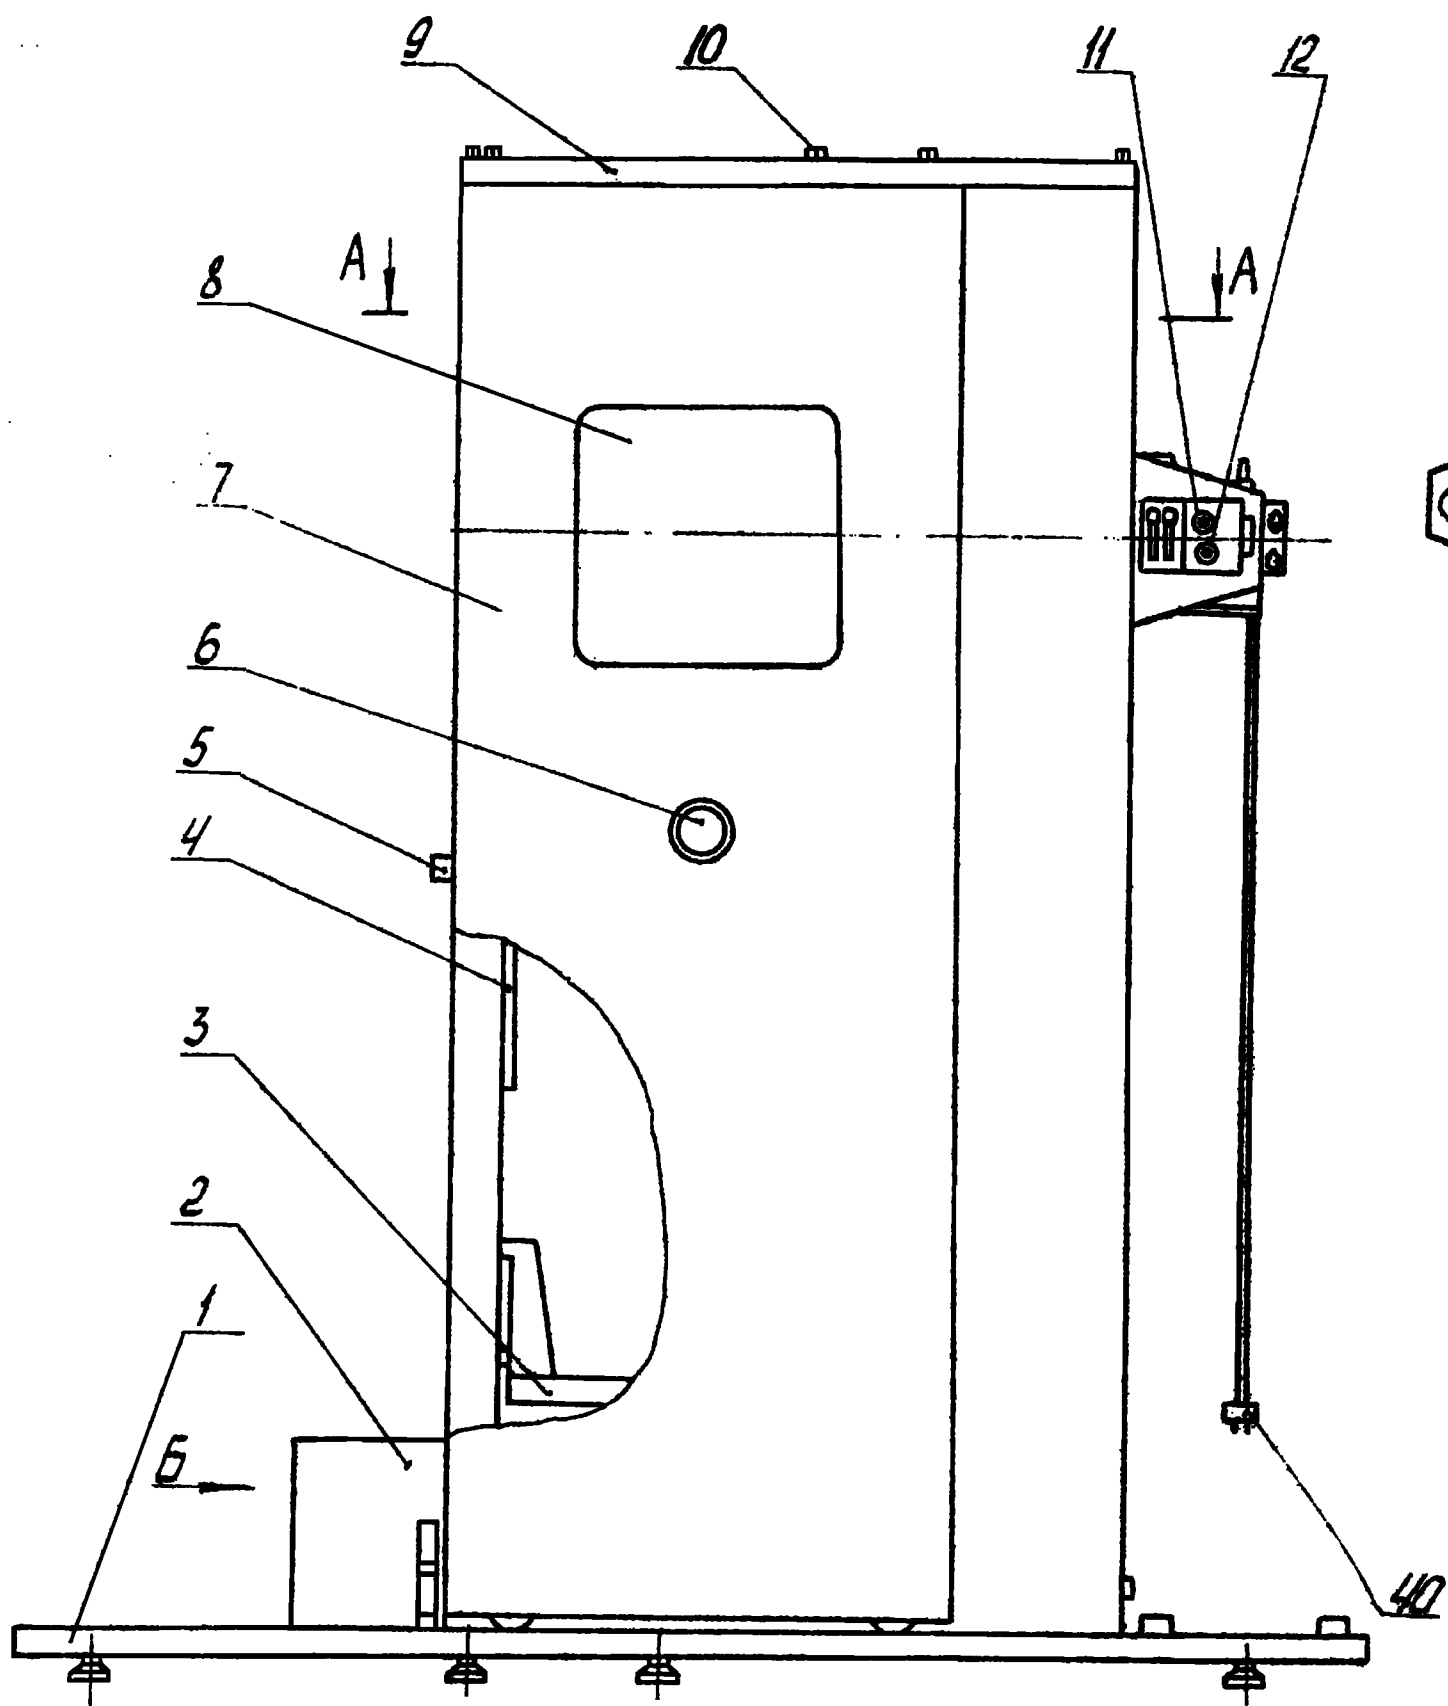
Кабина аппарата 12Φ7 Ц Сборочный чертеж .
